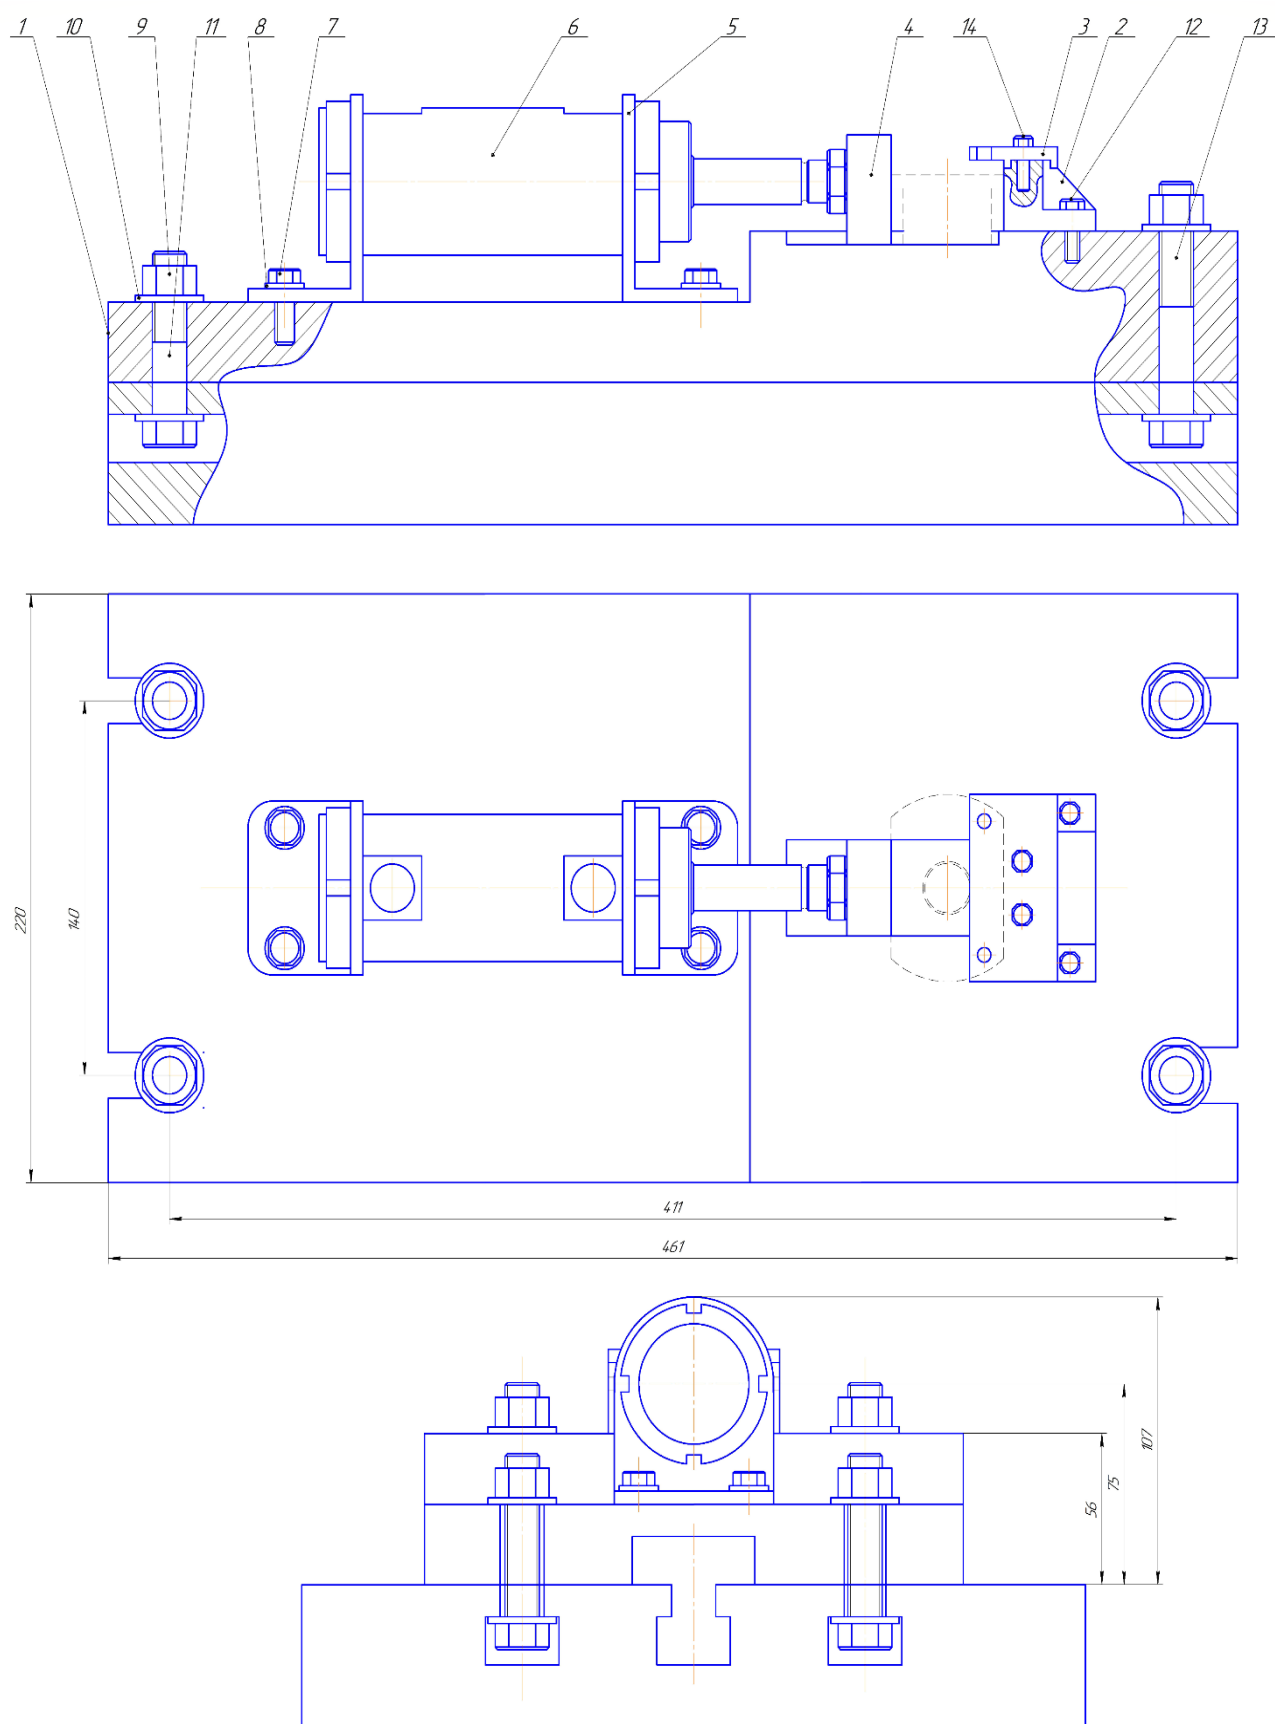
Компоновка (общий вид) приспособления для сверлильной операции.
